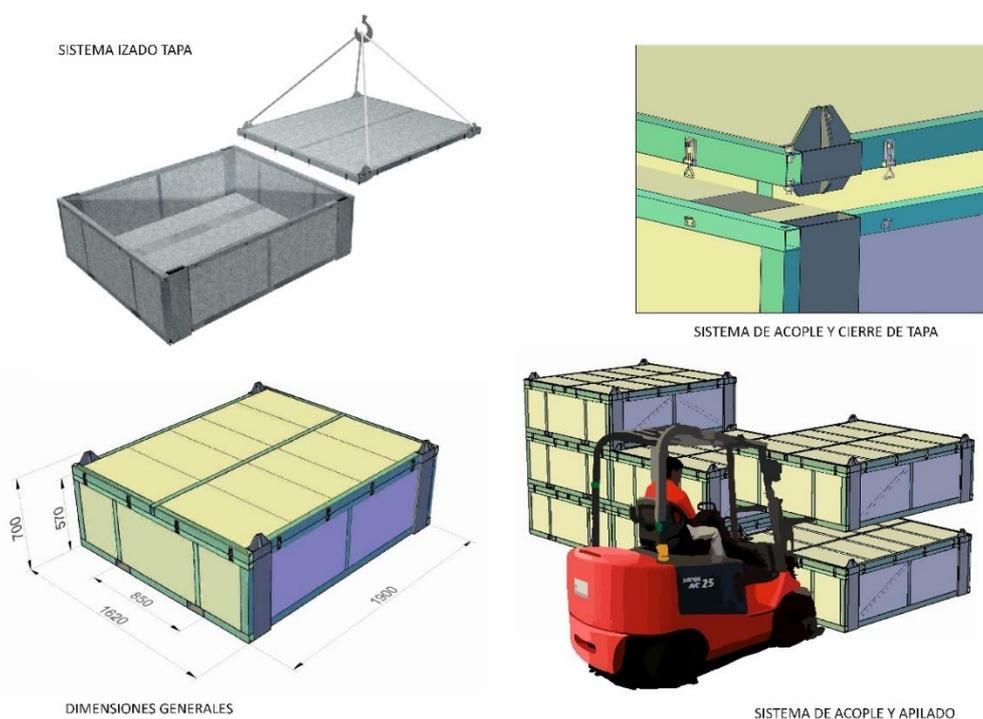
Plano de conjunto Embalaje TIPO A Pack de batería y TIPO B Módulos de batería (INDEREN, proyecto DIGICIRCULAR-BATT)
